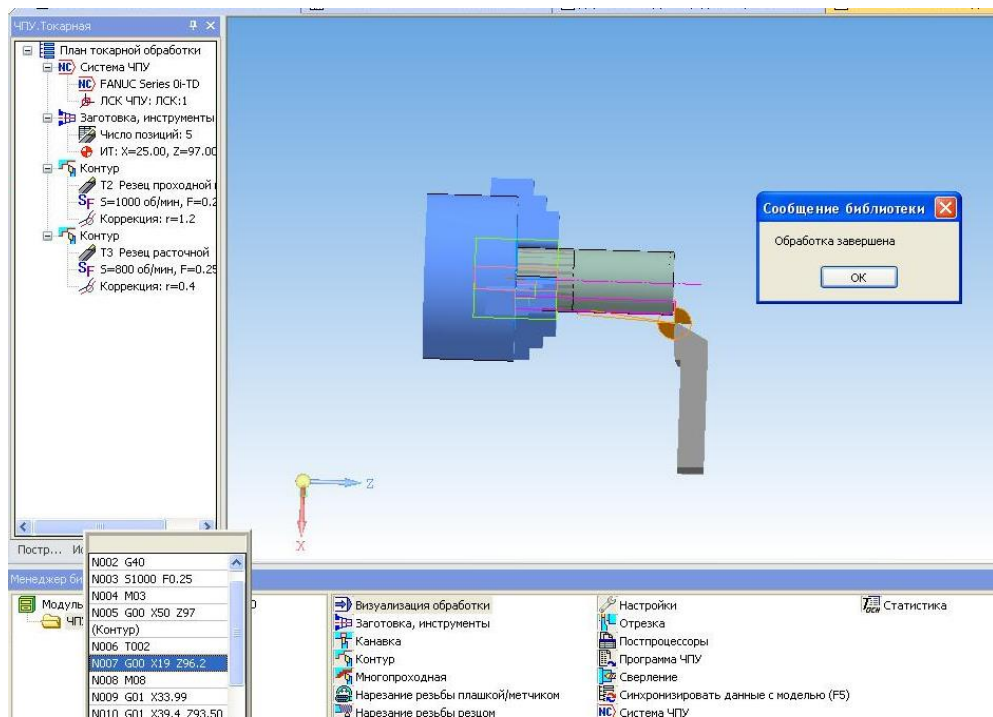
Процесс візуалізації токарної обробки заготовки
